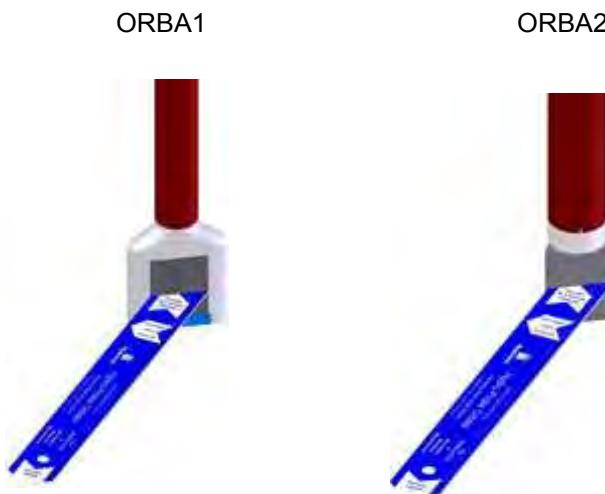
Приспособление для установки угла керамической лицевой пластины датчика Hydronix
